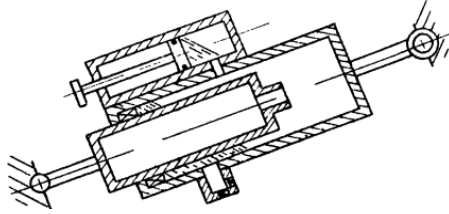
Пневматичний зрівноважувальний механізм із компенсатором
